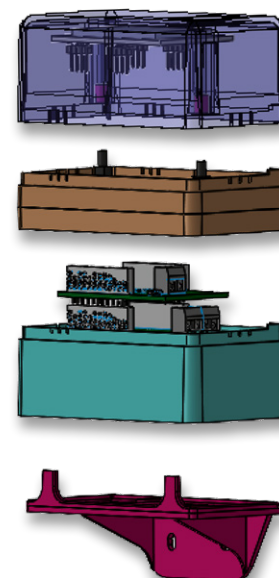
Explosionszeichnung des Gehäusesystems mit optionaler Gehäuseerweiterung (zur besseren Unterscheidung in verschiedenen Farben dargestellt)
